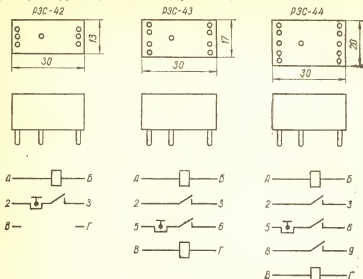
Габаритные чертежи и схемы реле типов P3C-42 — P3C-44.
